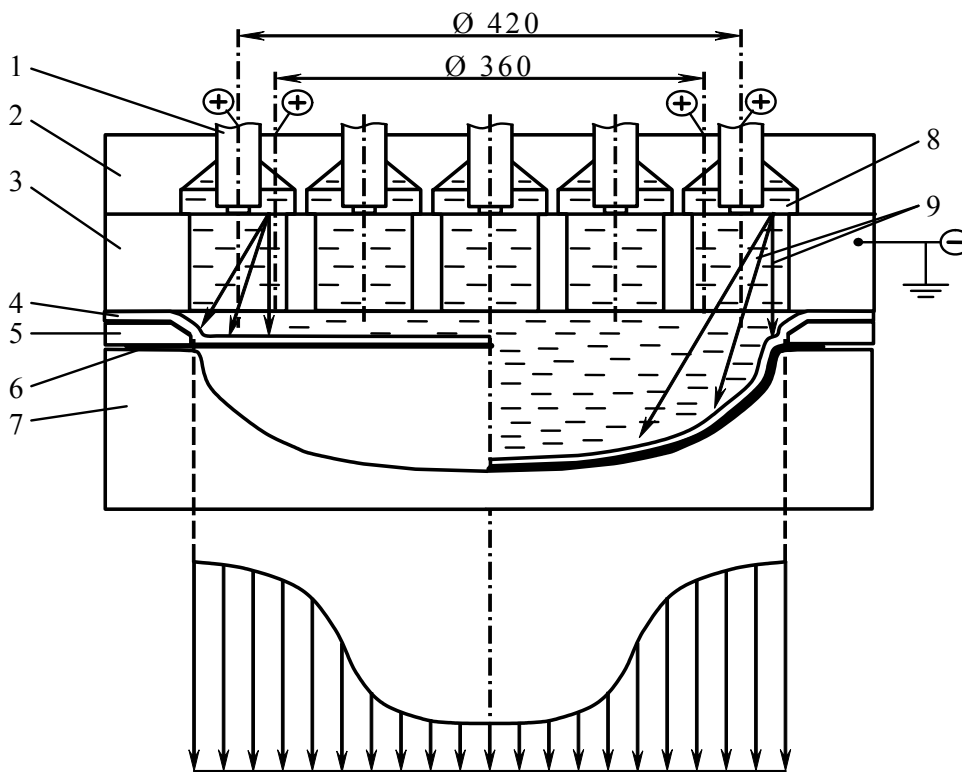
Схема штамповки и эпюра результирующего давления при штамповке в МРБ: 1 – электрод; 2 – плита с отражателями; 3 – плита с направляющими полостями – «массовый» электрод; 4 – эластичная диафрагма; 5 – прижимная плита; 6 – заготовка; 7 – матрица; 8 – вода; 9 – ударные волны
